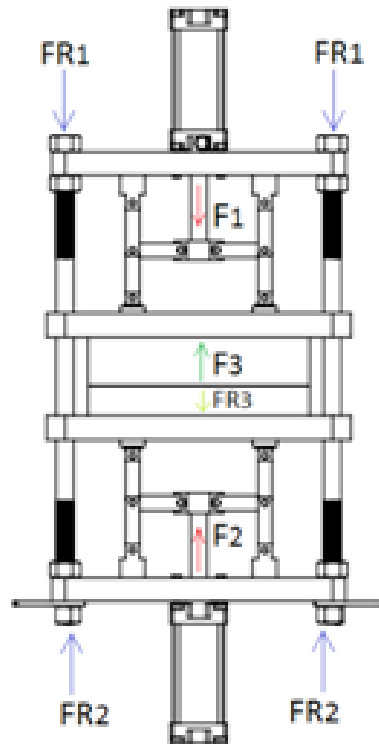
14: Esquema de cargas aplicadas en las columnas.
